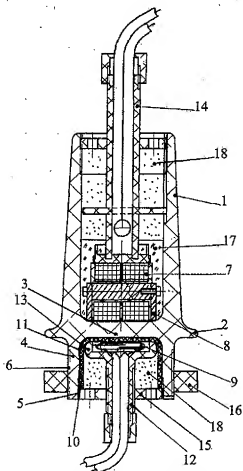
Конструкция реле ряда RG-75 и RG-50
